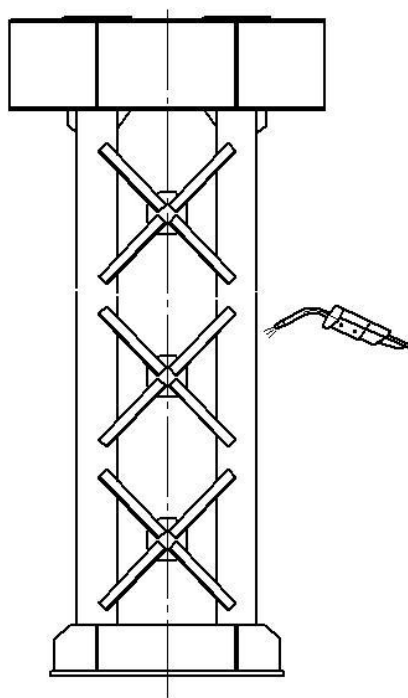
Условная схема выполнения технологических операций «сборка» и «сварка» для опоры
